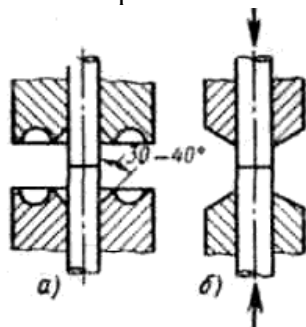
Схема зажимов для холодной стыковой сварки: а – с затрудненным истечением металла, б – со свободным истечением металла.
